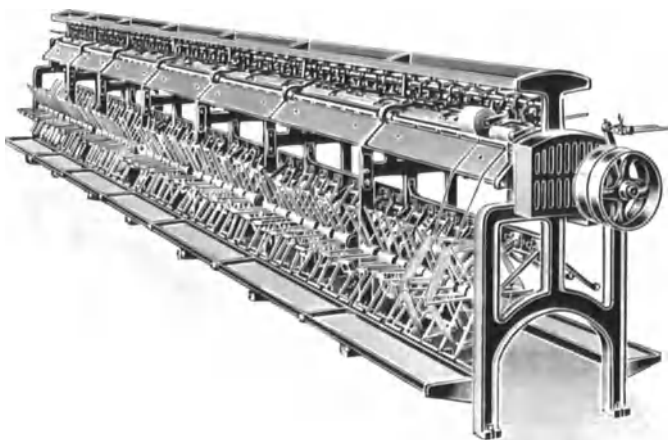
Zweiseitige Ketten-Kreuzspulmaschine.
